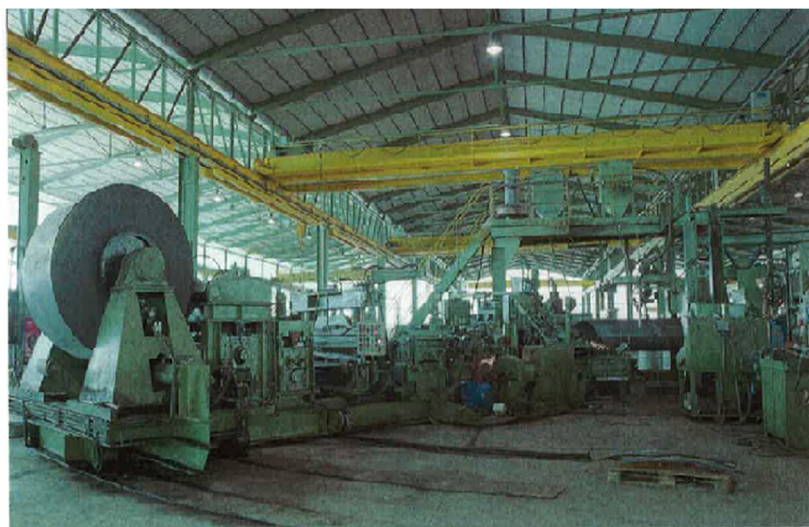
Machine de fabrication des tubes métalliques soudés en spirale.
